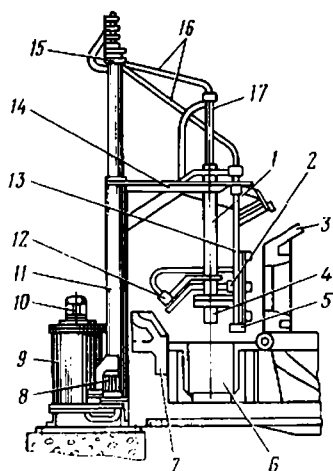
Устройство для окраски кокилей: 1 — пневмоцилиндр; 2 и 12 — форсунки; 3 — крышка кокиля; 4, 5 — емкость для краски; 6 — корпус кокиля; 7 — литниковая чаша; 8 — насос; 9 — бак; 10 — мешалка с приводом; 11 — стойка; 13 — кронштейн; 14 — консоль; 15 — дозатор для краски; 16 — трубки; 17 — полый шток
